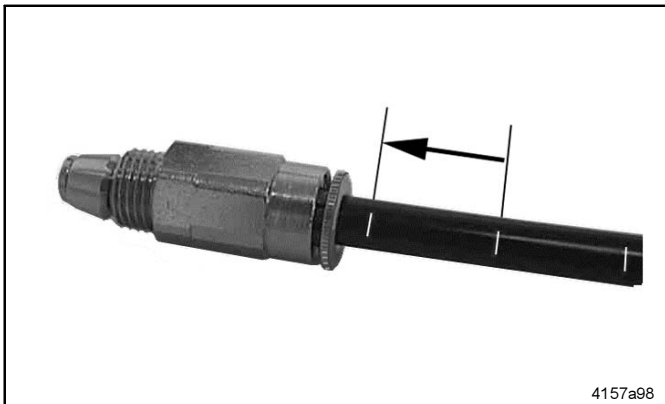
Rückschlagventil mit gerändelter Zange für Druckkunststoffrohr
